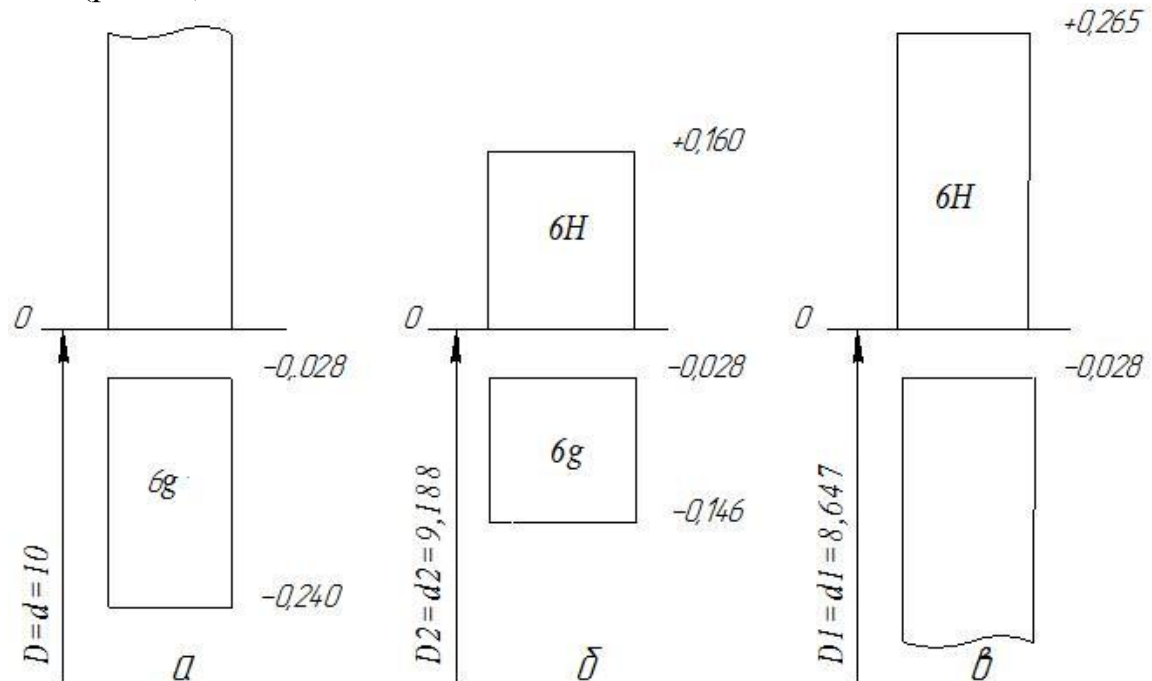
Схеми розташування полів допусків деталей різьбового з'єднання  $M10 \times 1,25 - 6H/6g$  по зовнішньому (а), середньому (б), внутрішньому (в) діаметрам.
